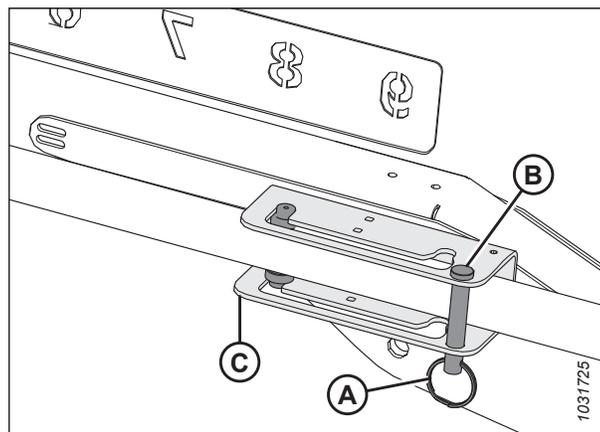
Réglage des vérins avant-arrière de type 2 – Position avant
